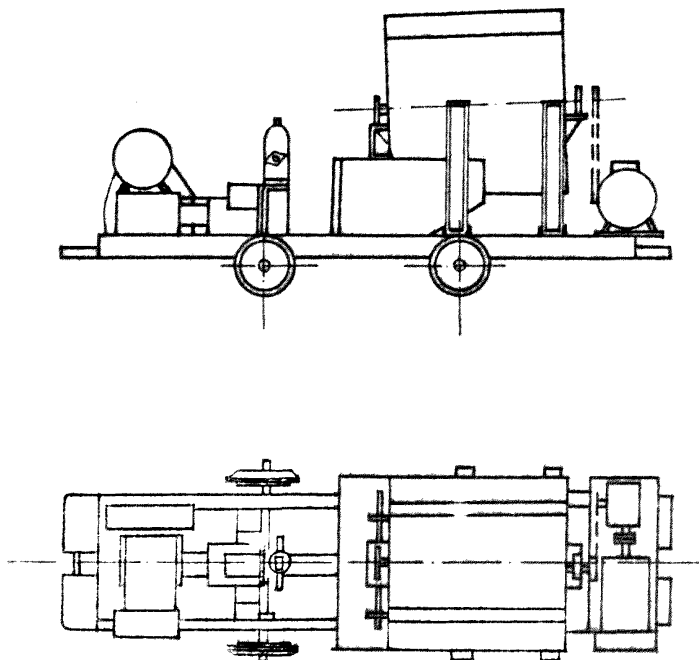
Установка для выполнения набрызгбетонных и инъекционных работ конструкции МакИСИ
